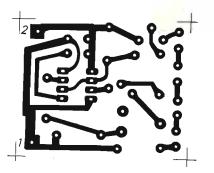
Disegno in grandezza naturale del circuito stampato da riprodurre su una delle due facce di una basetta-supporto, di forma rettangolare, delle dimensioni di 3,8 cm x 4,5 cm.
